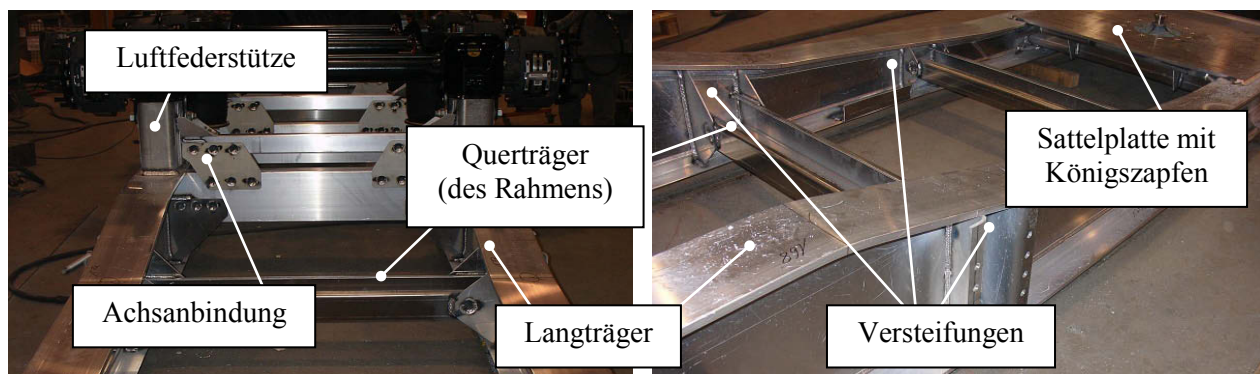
Geschweißter Leiterraum eines dreiachsigen Muldenkippers der Fa. MEIERLING GMBH &CO. KG aus Langträgern und Querträgern mit angeschweißten Achsanbindungen (links), vorderer Teil des Fahrgestellrahmens mit Schwanenhals und Königszapfen (rechts) (Die Rahmenunterseite zeigt bei der Montage stets nach oben.)
